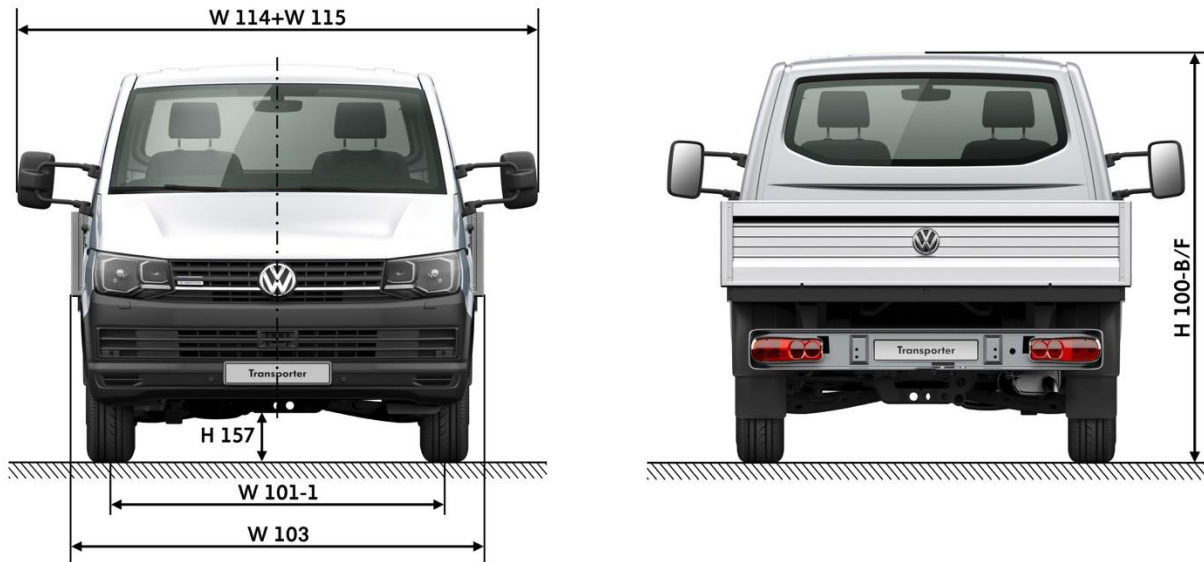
Размеры бортового автомобиля, короткая и длинная база
